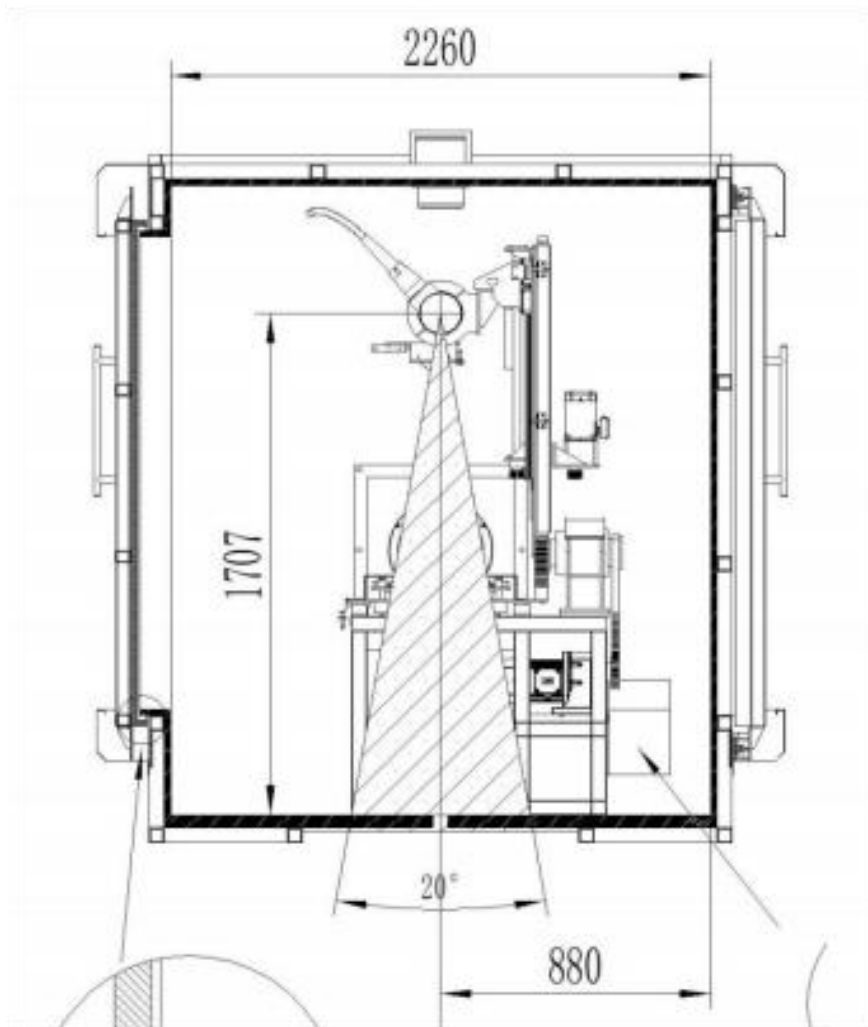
单管 DR2 探伤铅房剖面布局图（单位：mm）
